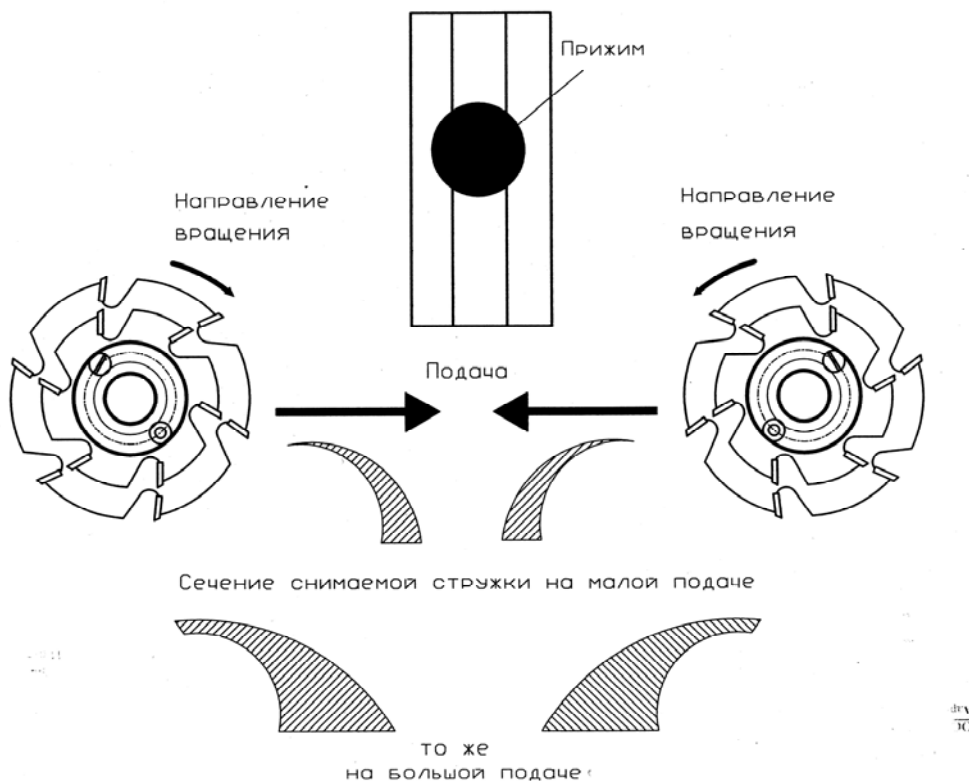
Схема фрезерования торца импоста с оптимальным выбором направления вращения и подачи фрезы.
